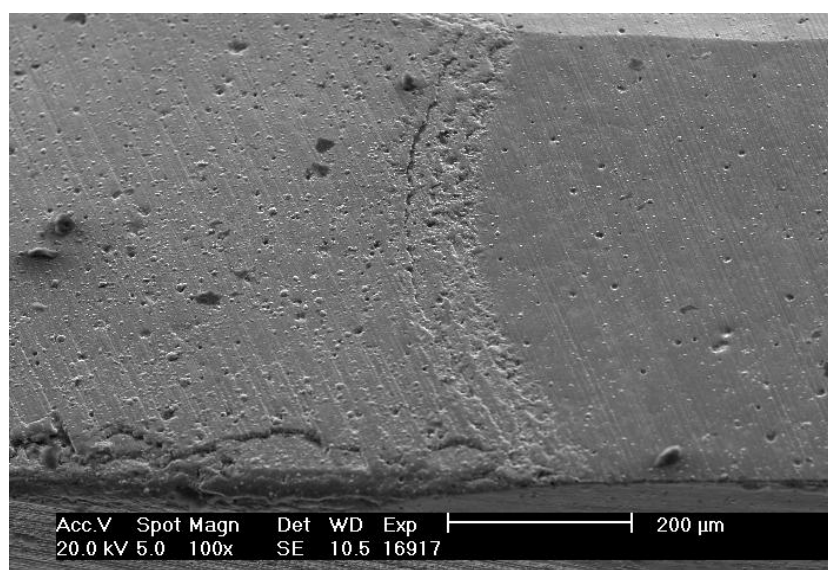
Detail povrchu bříty, zvětšeno 50x
